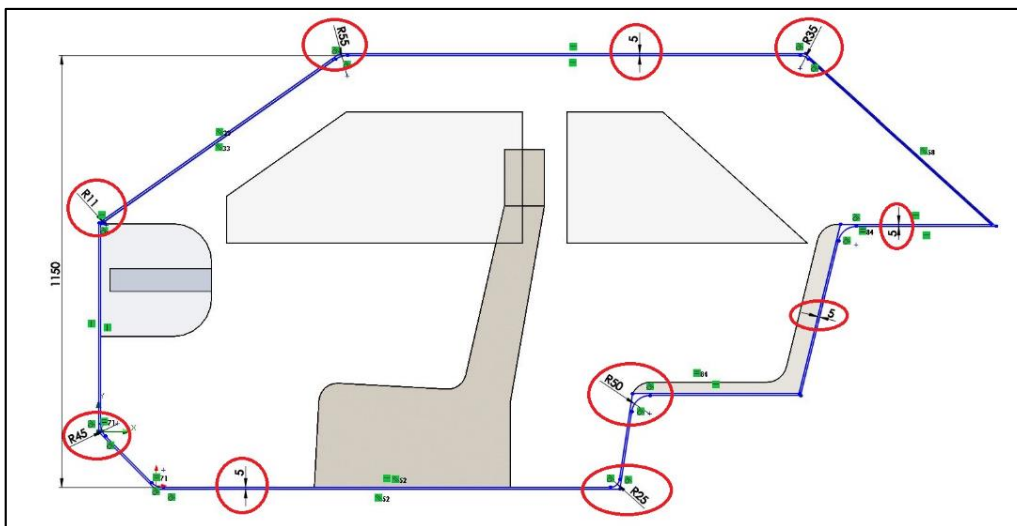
Modificação das arestas e da espessura da estrutura.
